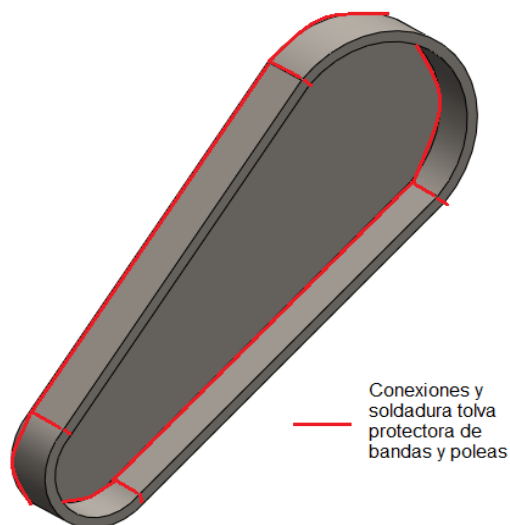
Conexiones y soldadura protección de bandas y poleas.
